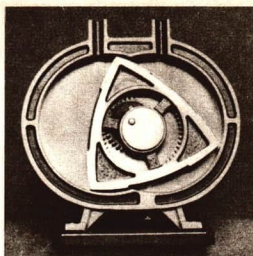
/1 Schnittmodell eines Drehkolbenmotors
